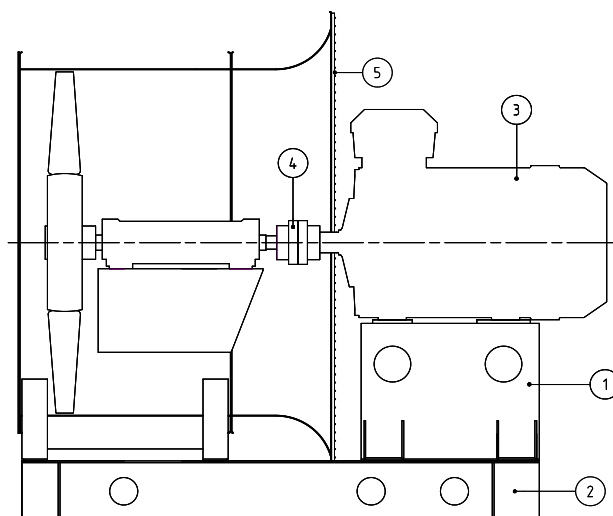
Assemblaggio di ventilatore assiale esecuzione 8
